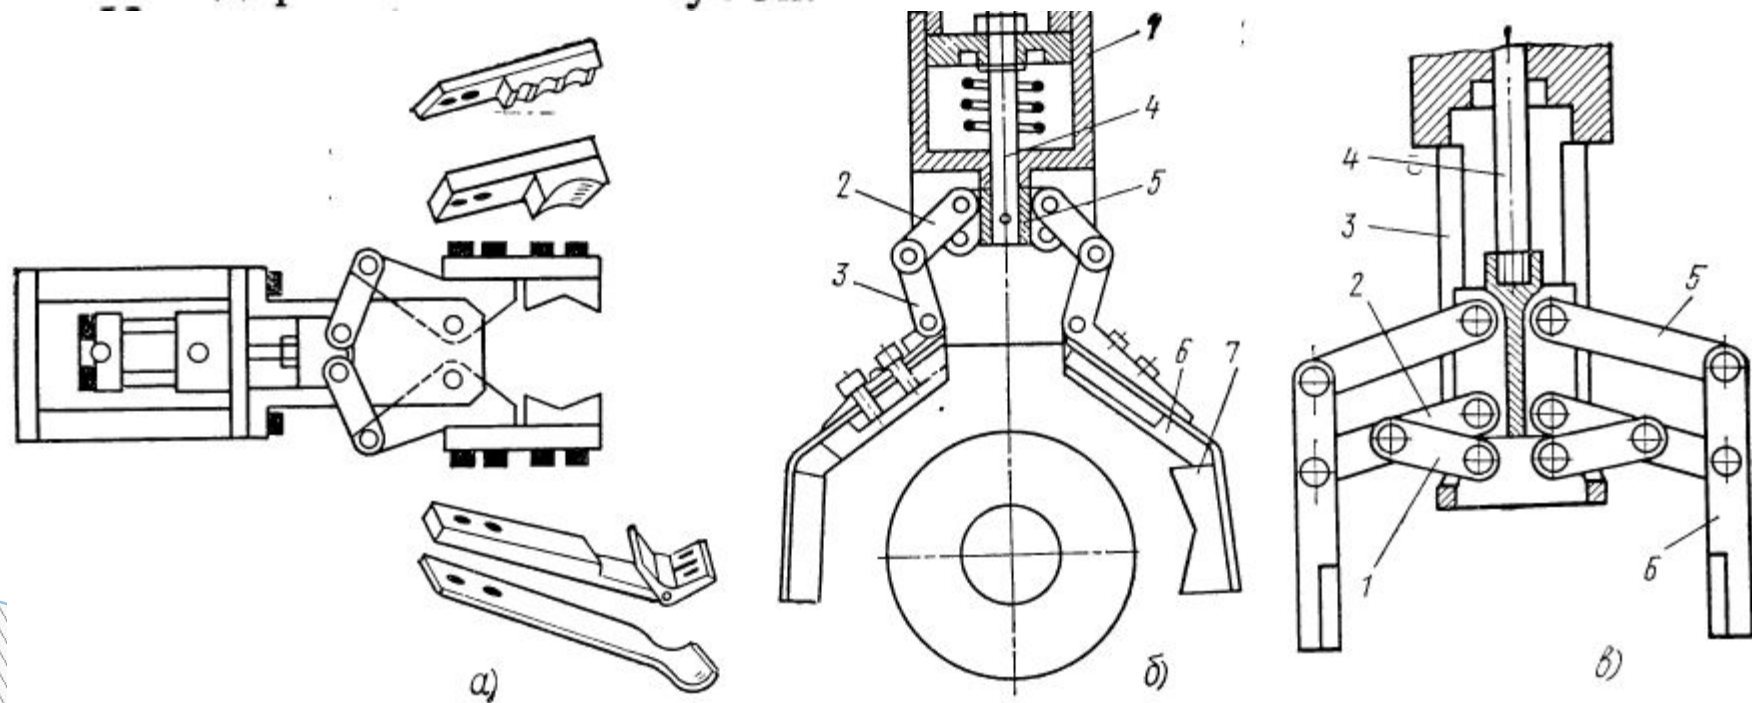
Широкодиапазонные пневматические рычажные захватные устройства
